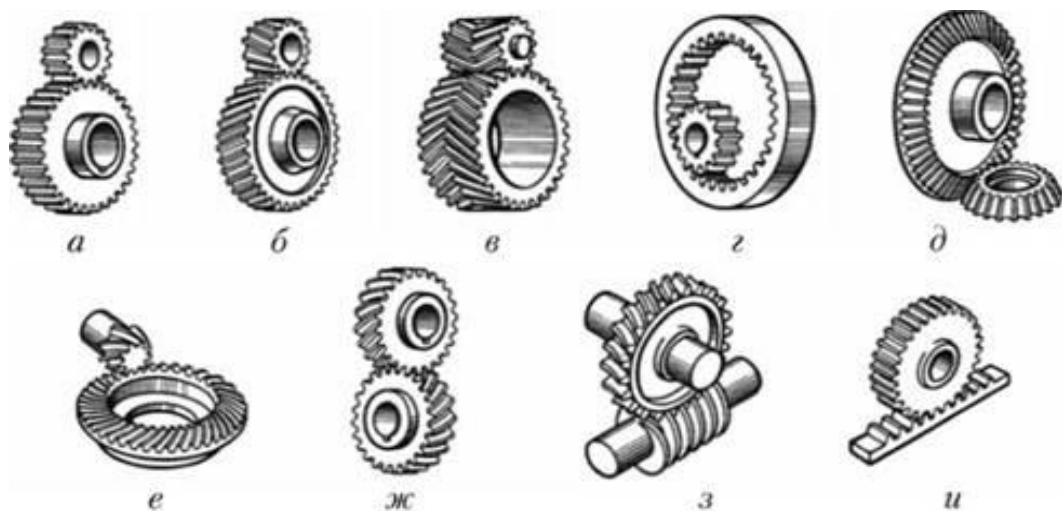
Схематичне зображення зубчастих передач. а - циліндрична прямозуба; б - циліндрична косозуба; в - циліндрична шевронна; г - циліндрична з внутрішнім зачепленням; д - конічна прямозуба; е - конічна з криволінійними зубами; ж - циліндрична гвинтова; з - черв'ячна; і - рейкова.
